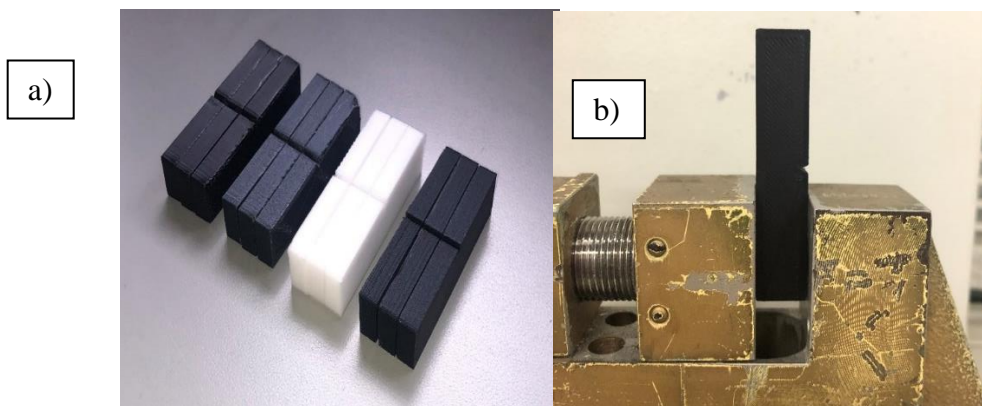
a) Muestras de impacto fabricadas bajo modelo de impresión 3D. b) Probeta en máquina de ensayo al impacto método Izod, según norma D256 – 10, Fuente: Autor.
